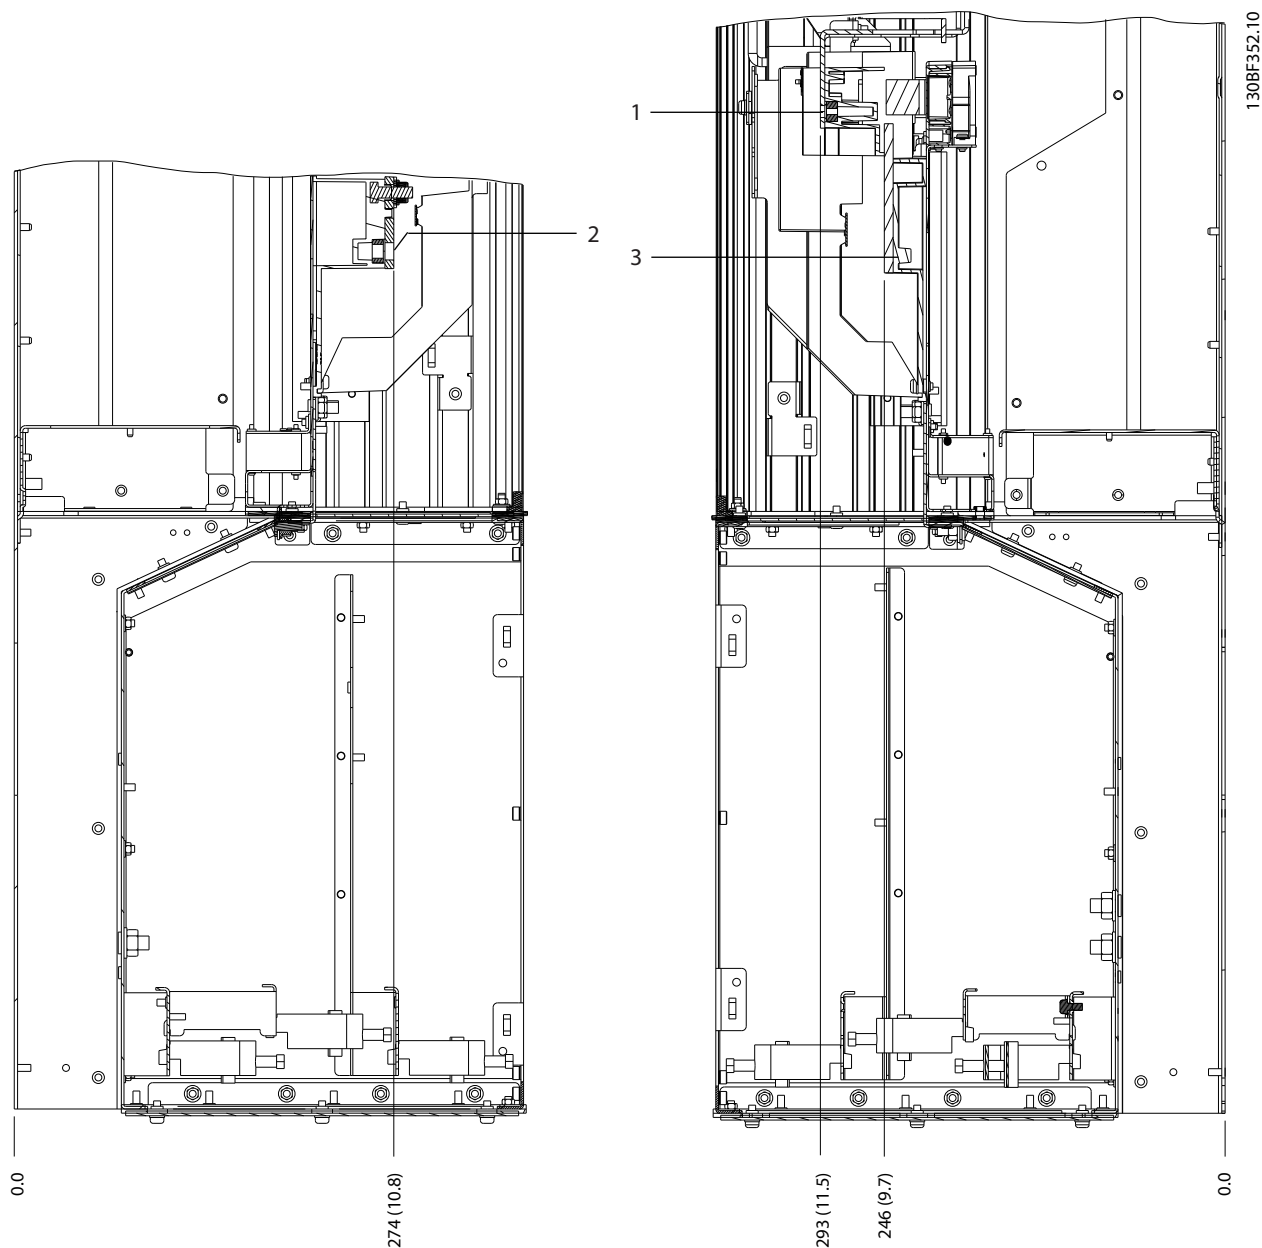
Dimensions des bornes D5h avec option sectionneur (vues latérales)
